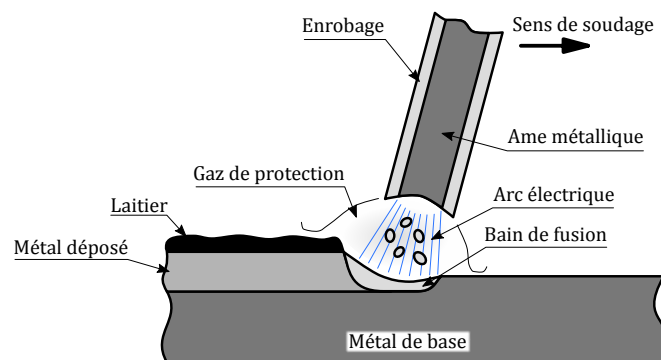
Principe du soudage à l'électrode enrobée
